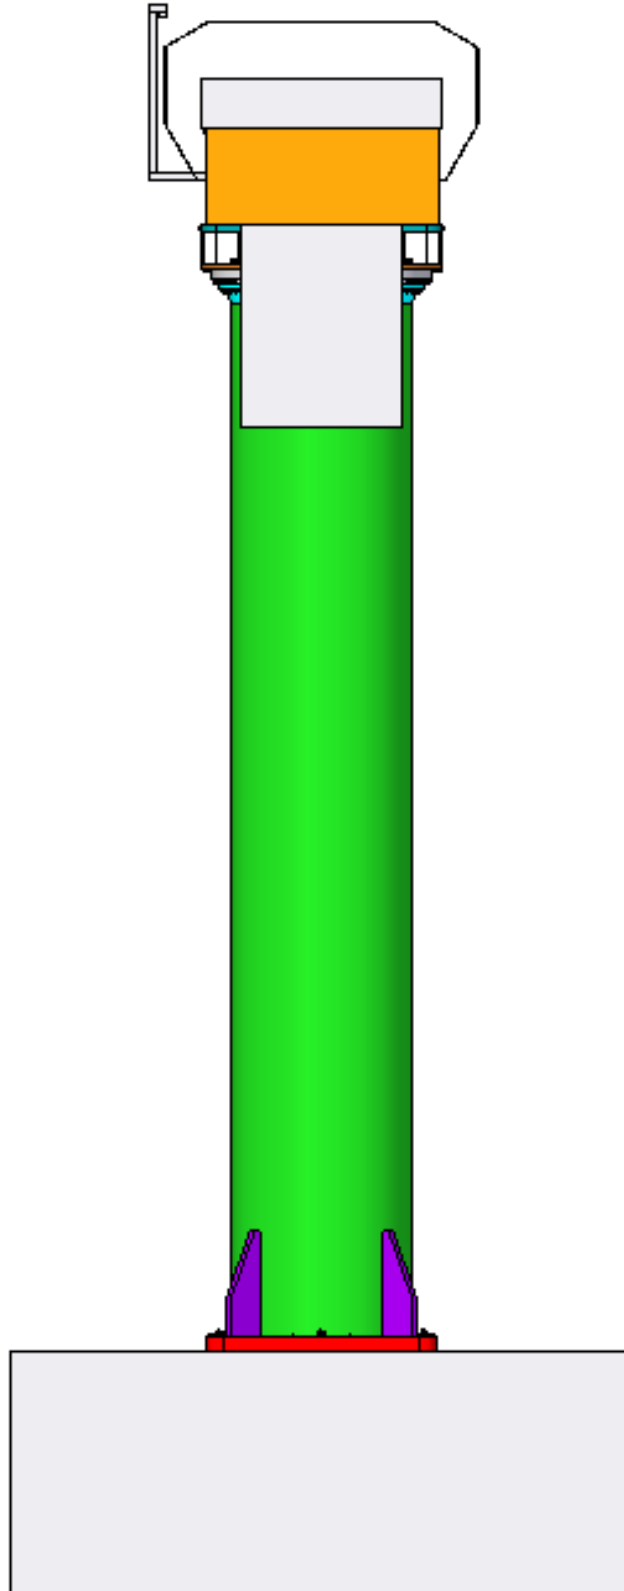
Grúa portuaria para elevación de embarcaciones (alzado).
